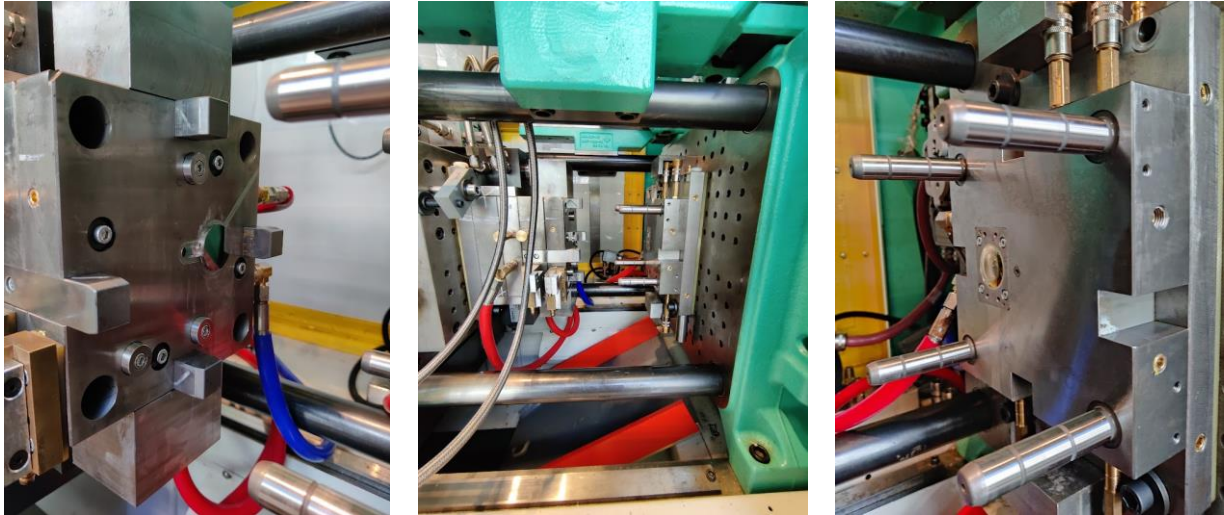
Links: Auswerferseite des Spritzgusswerkzeugs, Mitte: Das Spritzgusswerkzeug eingebaut in der Anlage, Rechts: Die Einsatzseite des Werkzeugs
